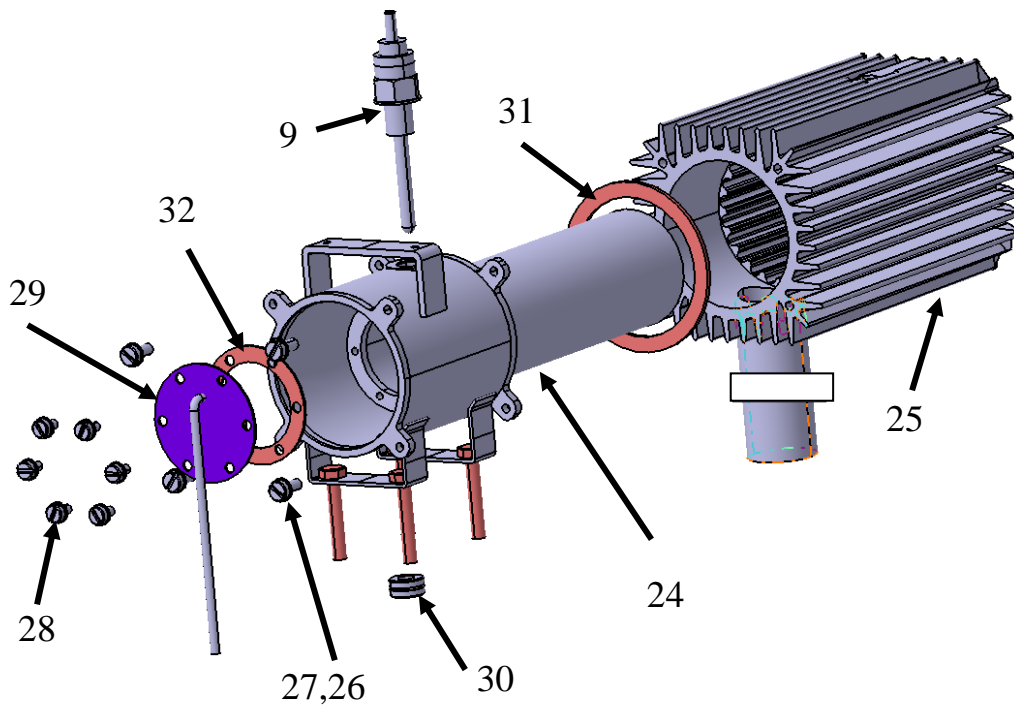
Desen subansamblu arzător, schimbător de căldură 3D explodat
